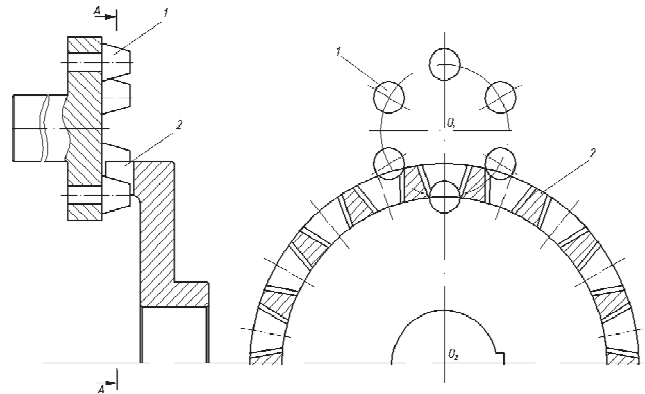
Торцевая зубчатая передача внешнего зацепления.
